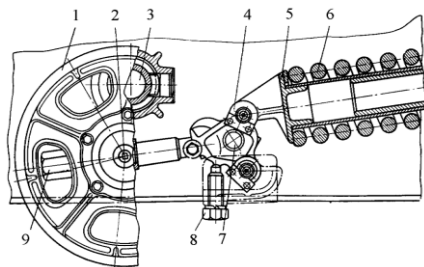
Амортизационно-натяжное устройство: 1 – направляющее колесо; 2 – ось; 3 – кривошип; 4 – блок шарниров; 5 – шток; 6 – пружина; 7 – ось; 8 – упорный винт; 9 – натяжной винт
